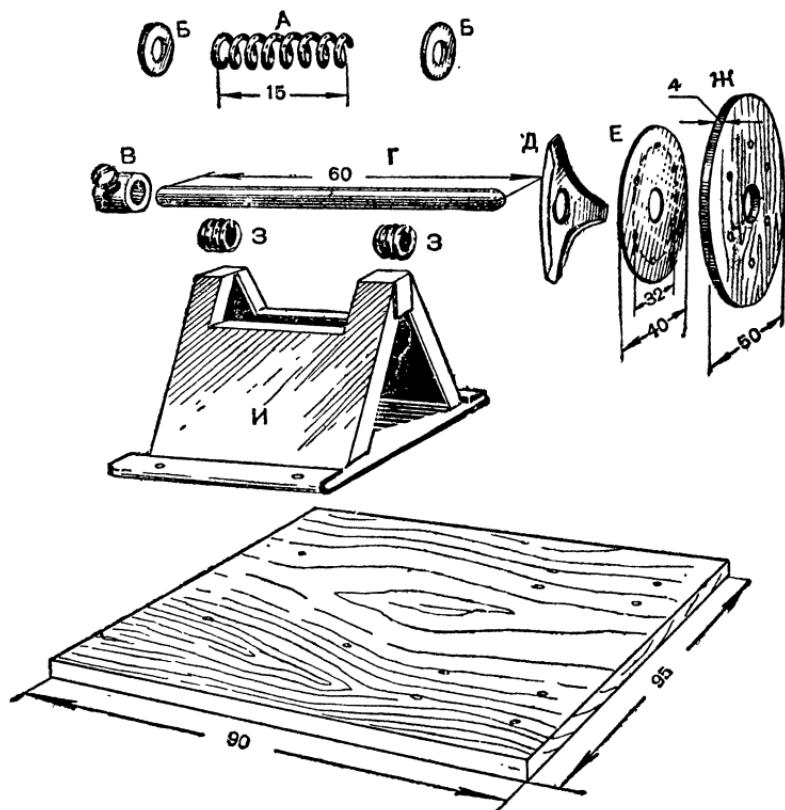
Детали редуктора № 4 (рис. 114): *А* — прижимная пружина; *Б* — металлические шайбы; *В* — втулка с винтом; *Г* — вал; *Д* — «паук»; *Е* — накладка диска; *Ж* — диск; *З* — подшипники; *И* — стойка диска.
